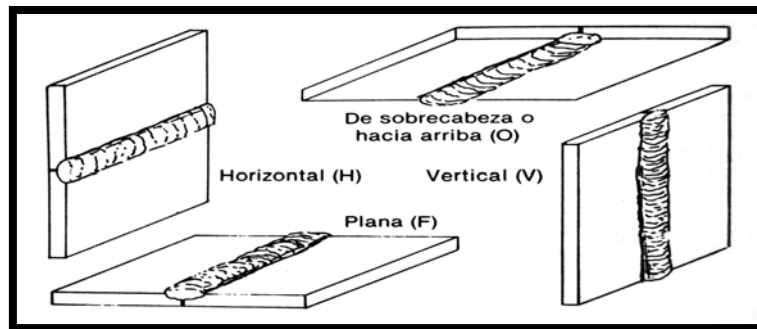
Muestra de las cuatro posiciones básicas de soldadura
